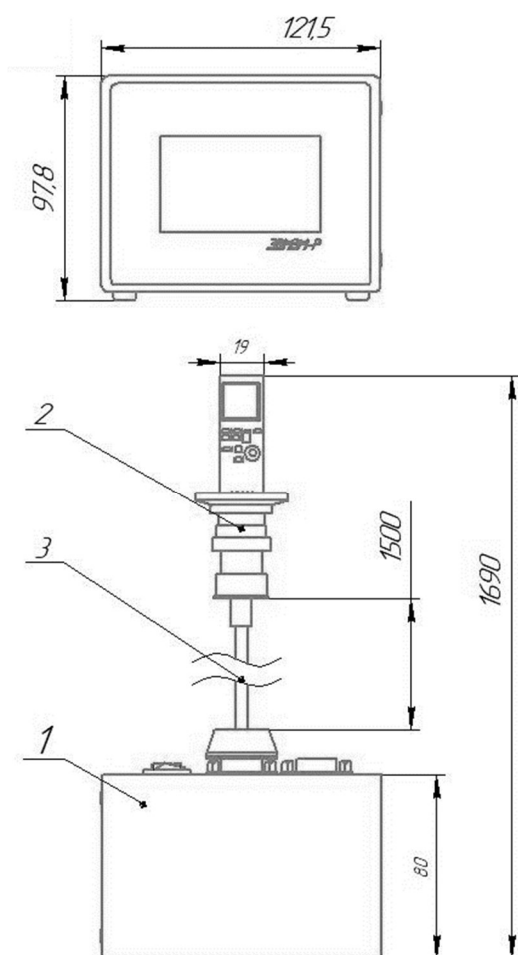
Габаритный чертеж корпуса преобразователя
